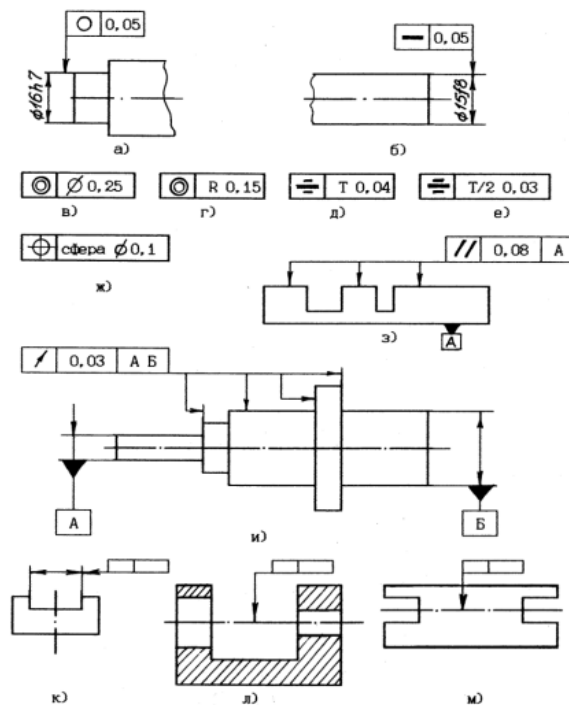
Варіанти вказівки допусків форми і розташування на кресленнях.
